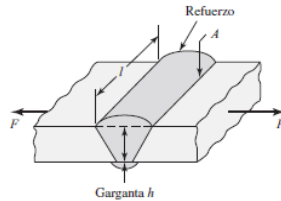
Dimensiones de una soldadura a tope sujeta a una carga de tensión [31].
